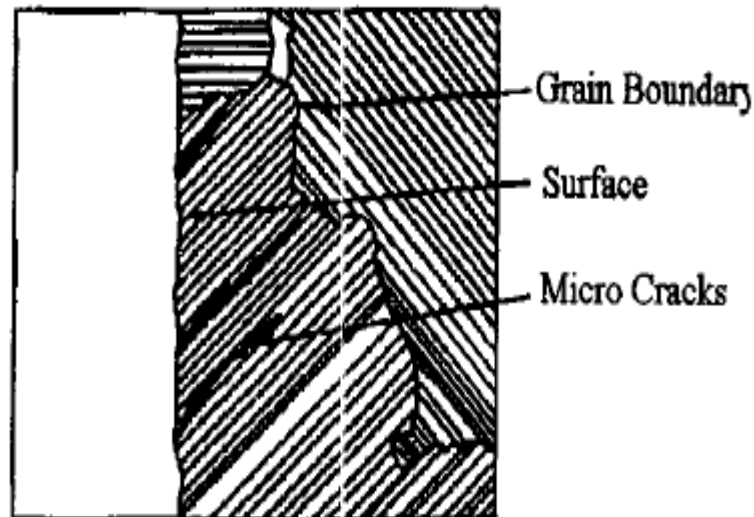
Agrietamiento en una junta soldada.
